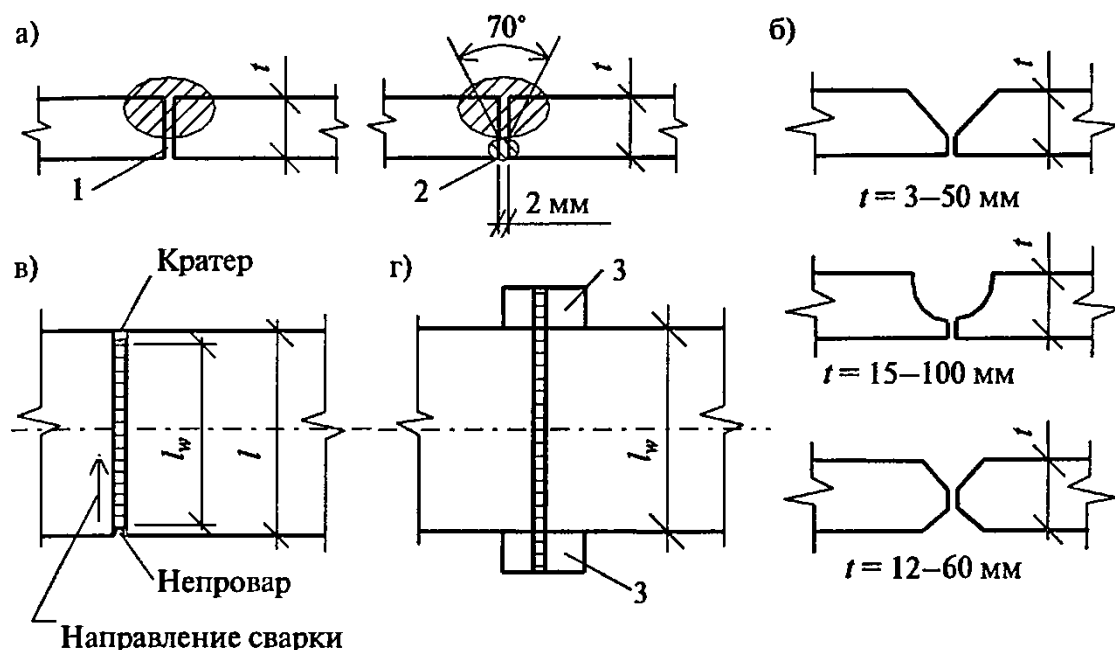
Выполнение сварных соединений: а) подварка корня шва; б) разделка кромок соответственно: V-образная, U-образная, X-образная; в) образование непровара и кратера по длине шва; г) выполнение шва на технологических подкладках; 1 — непровар корня шва; 2 — подварка корня шва; 3 — технологические подкладки
